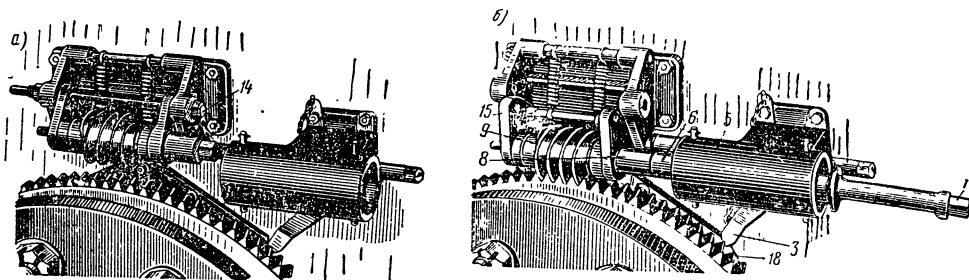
Общий вид валоповоротного механизма (обозначения см. на рис. 116):
